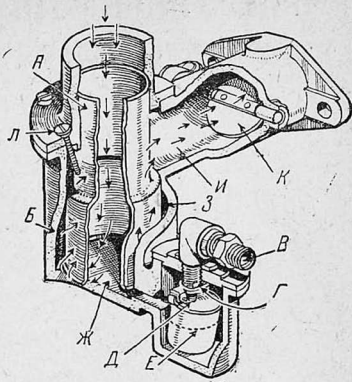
Общий вид испарительного карбюратора Инвикта с частичными разрезами
